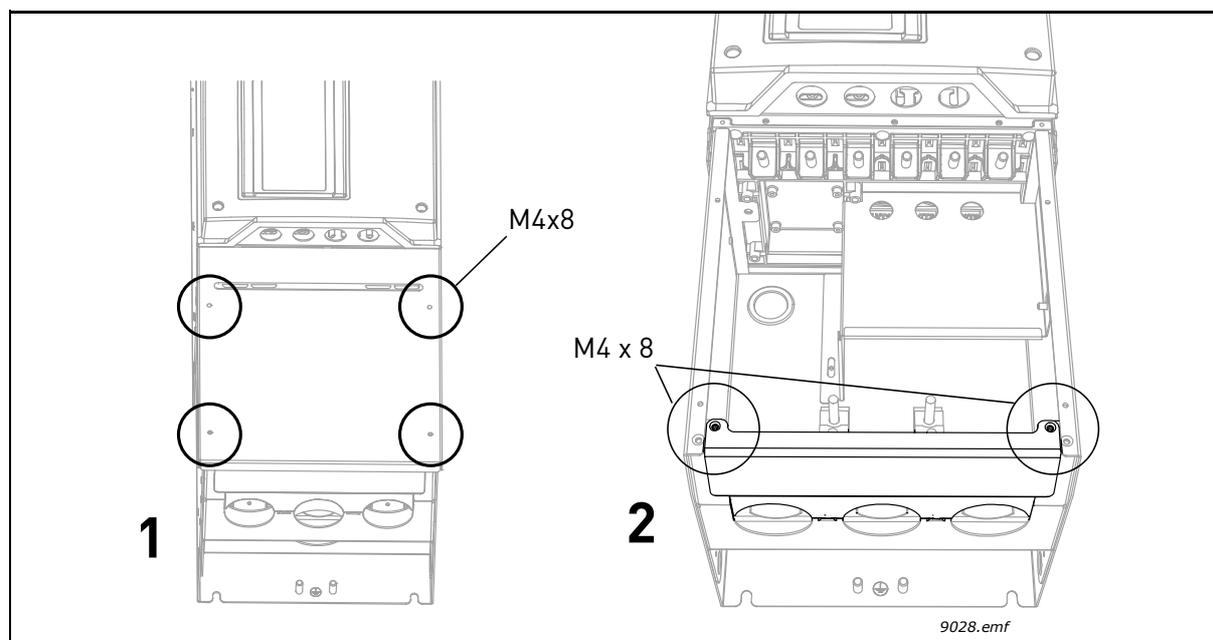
Extracción de la tapa de cables y la placa de fijación de cables (MR8).
